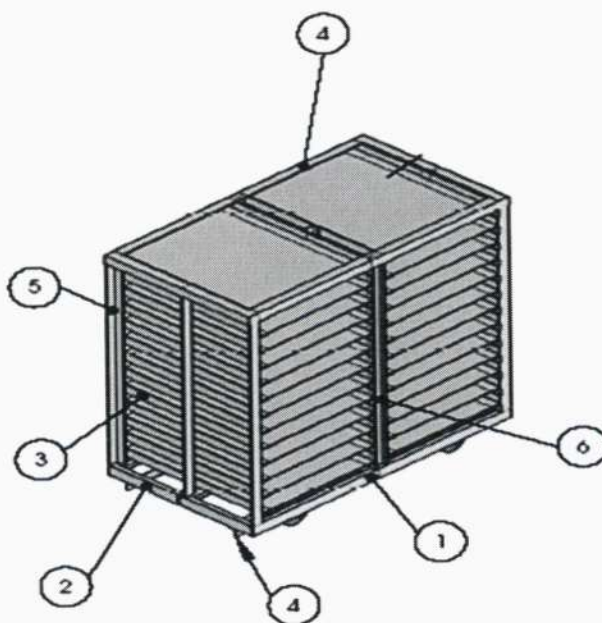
Componentes estruturais da vagoneta. Fonte: Acervo Pessoal, 2011.
